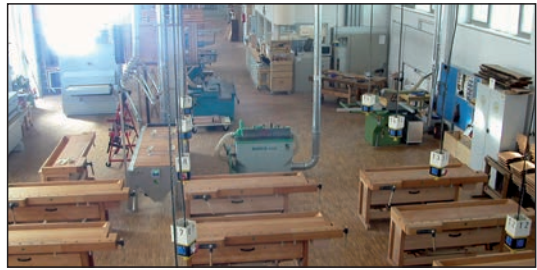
Bankraum einer Lehrwerkstatt mit angeschlossenem Maschinenraum
